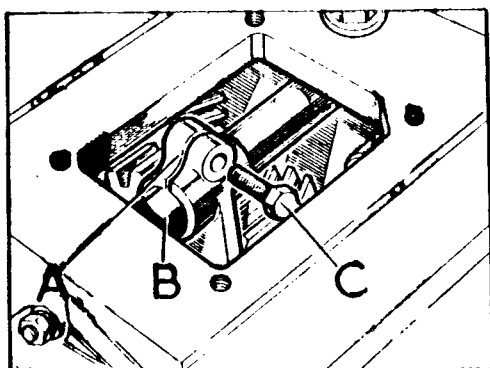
Conjunto de la horquilla selectora de la caja reductora
